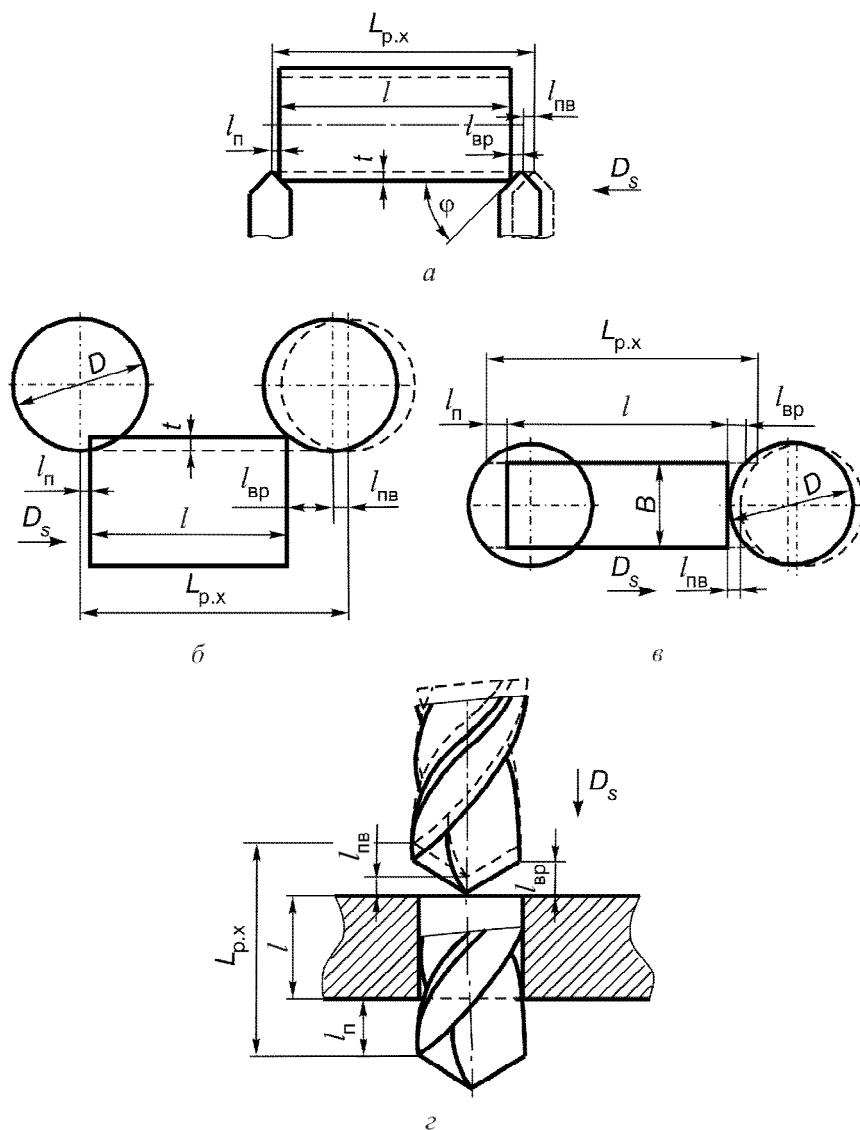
Схемы для определения рабочего хода инструмента при точении (а), фрезеровании (б, в) и сверлении (з)
